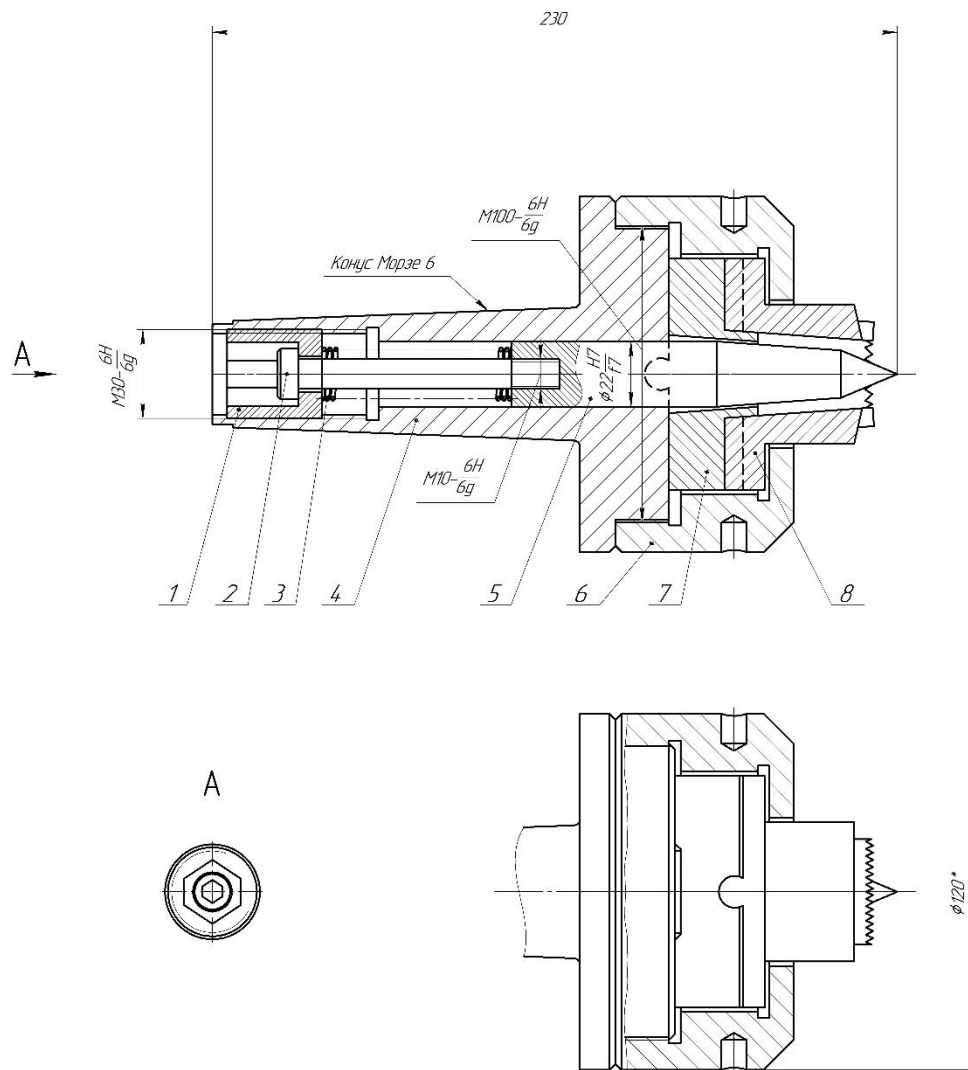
Патрон торцевий: 1 – гайка задня; 2 – шток; 3 – пружина; 4 – корпус; 5 – плунжер; 6 – гайка корпусу; 7 – конус; 8 – напрямна;
